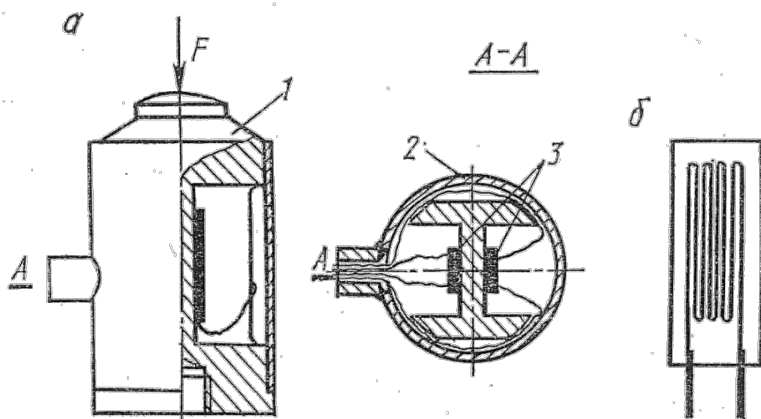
Тензорезисторный измерительный преобразователь больших сил
